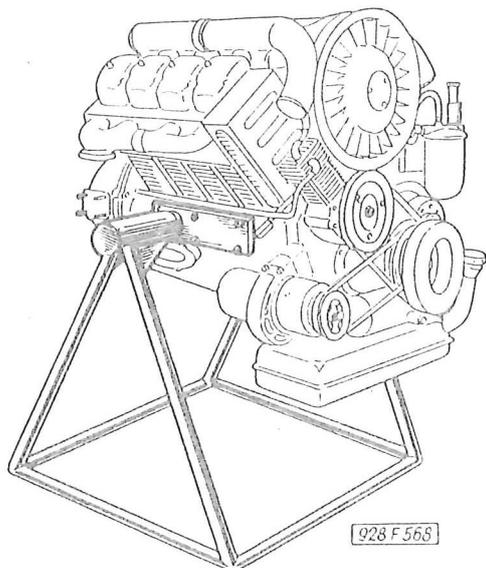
Auflegen des Motors auf dem Montageständer PRM-0729
